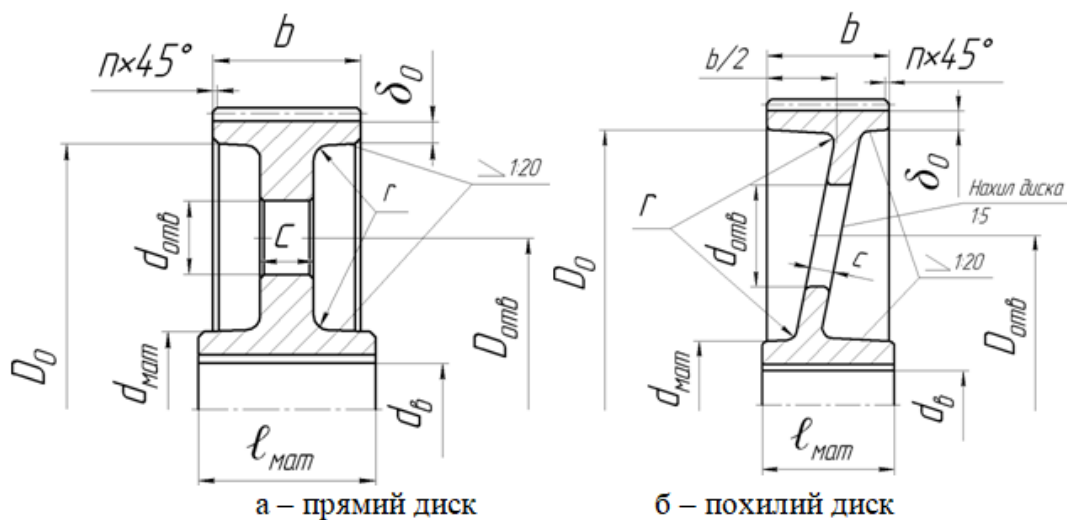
Конструкція циліндричного зубчастого колеса виготовленого за допомогою литва
